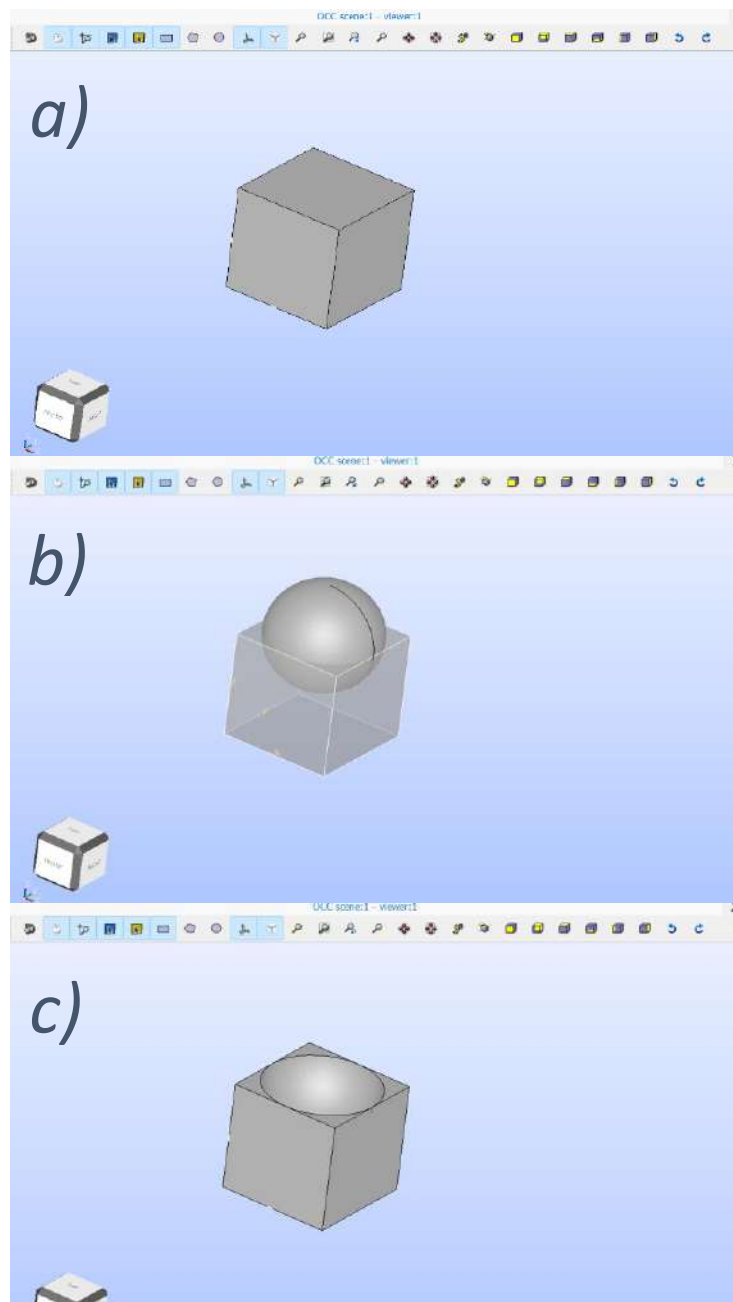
a) Pièce à découper b) l'outil de découpe c) pièce coupée
